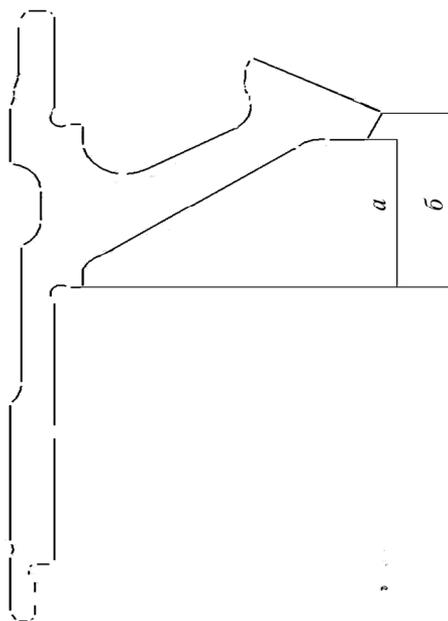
Эскиз спирально-конического зубчатого колеса с обозначением наблюдаемых размеров:
